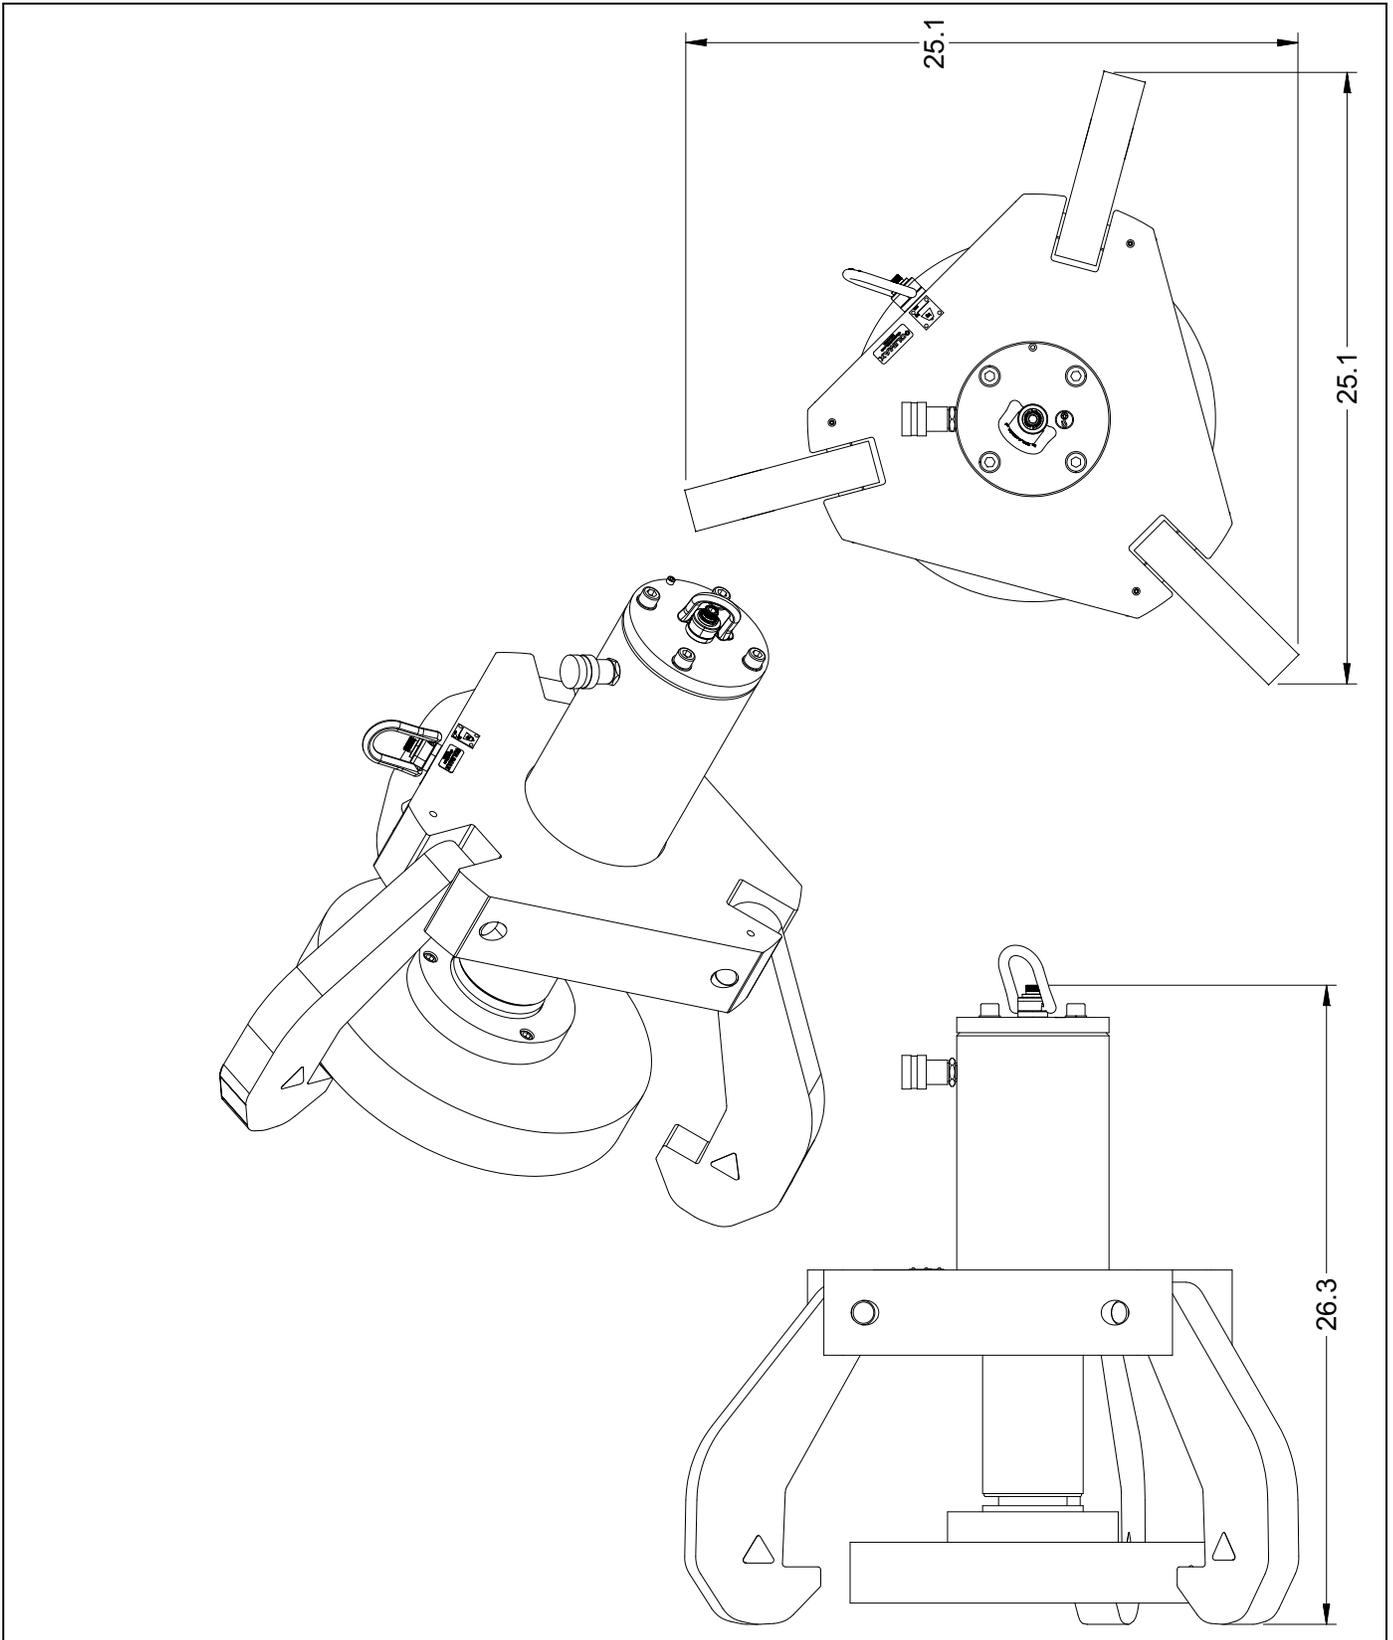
DIMENSIONS DE LA HFS-14
